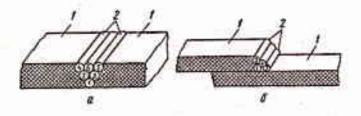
Стыковое (а) и раструбное (б) соединения: 1— соединяемые трубы; 2— сварные швы
